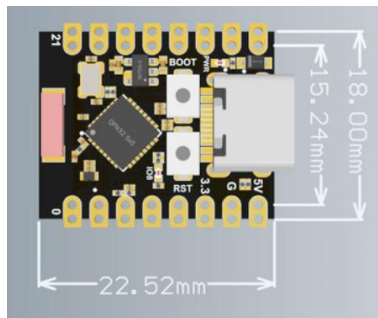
Placa ESP32-C3-SuperMini. Fuente (espboards, 2025)
